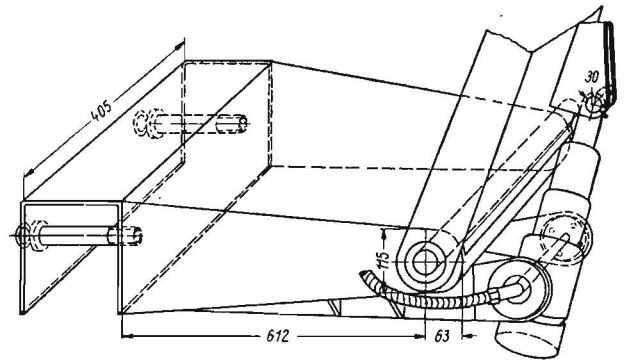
Der Hauptträger (Draufsicht, Maße in mm)
